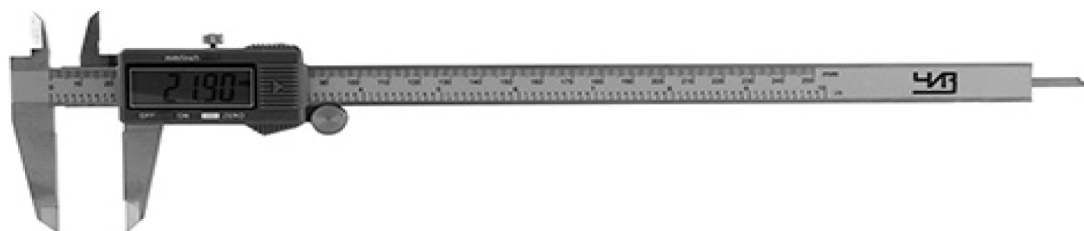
Общий вид штангенциркулей ШЦЦ-I
